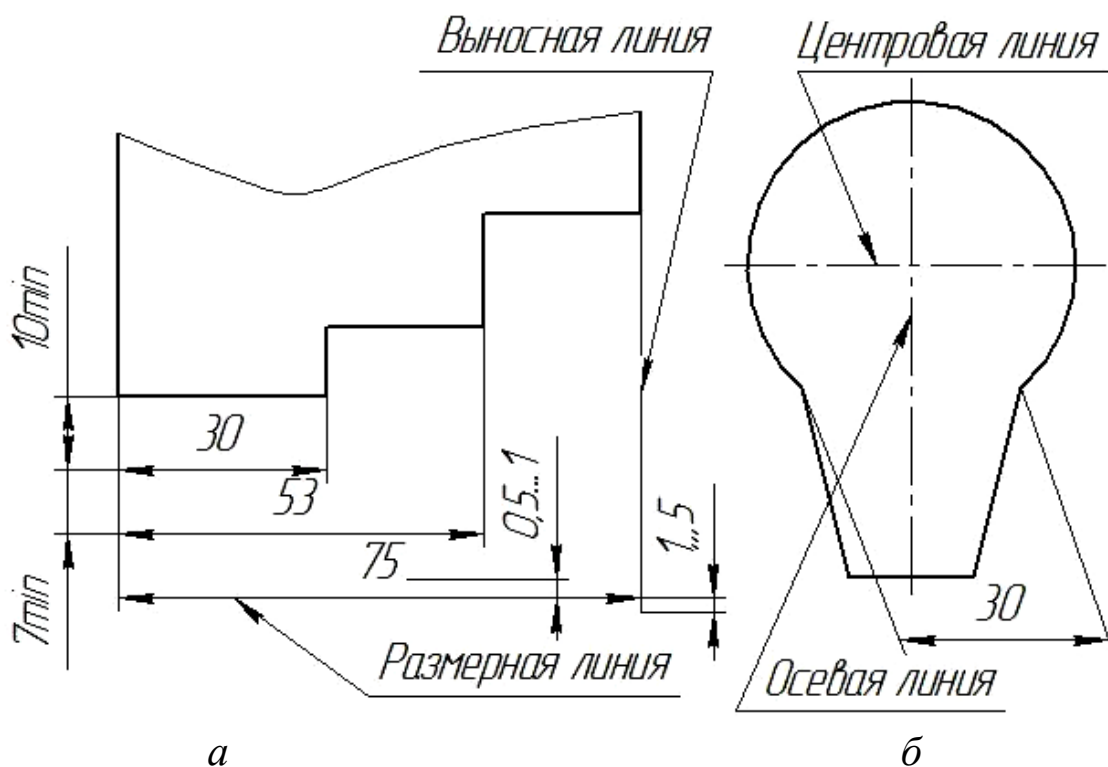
Расположение на чертеже размерных линий и чисел
